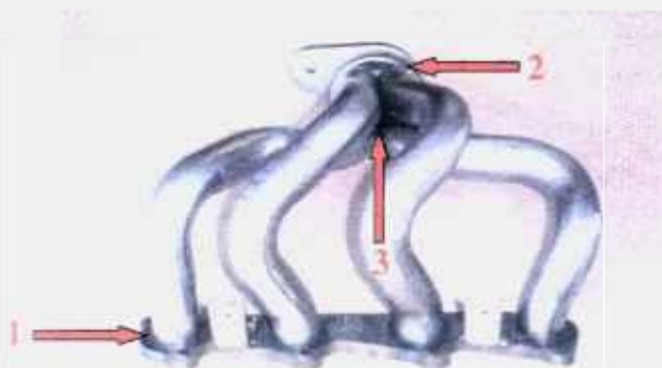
Foto de um *manifold* tubular confeccionado com o aço 441. Os pontos indicados correspondem: (1) - lado do motor: cada tubo com o respectiva flange; (2) - lado oposto do motor: junção dos 4 tubos; (3) - cordão de solda utilizado para unir tubos entre si.
